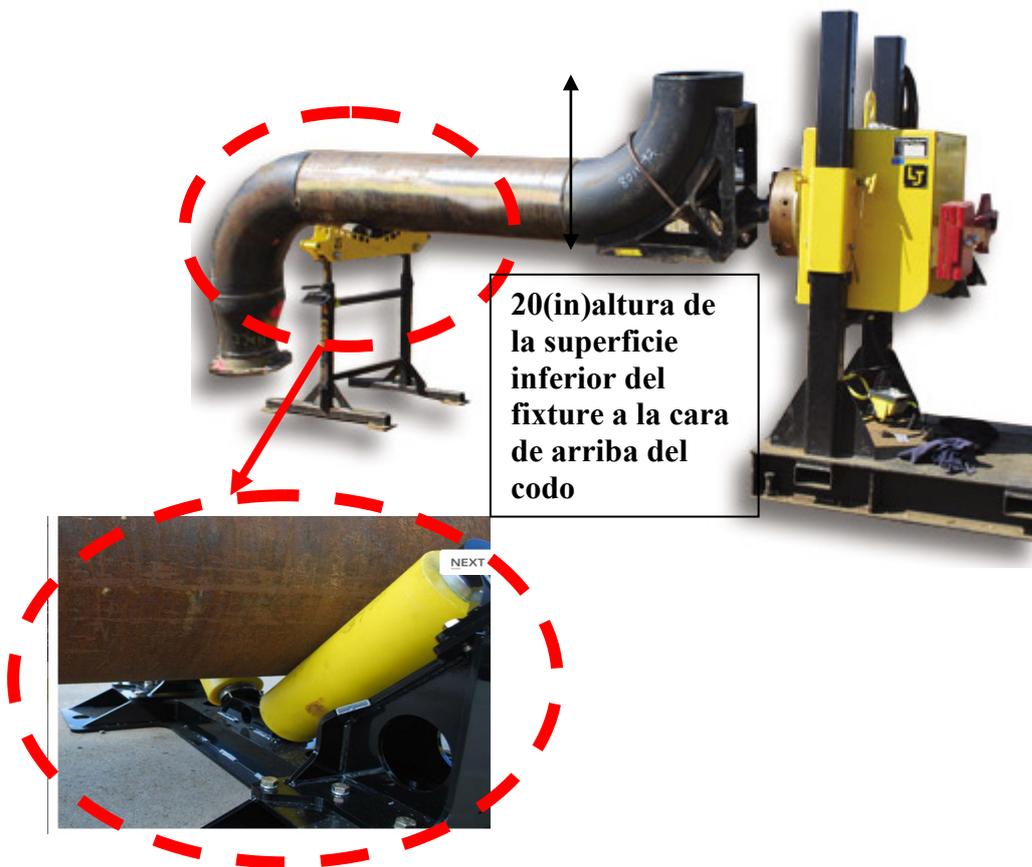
Medidas importantes en la interface con la zona de soldado.
